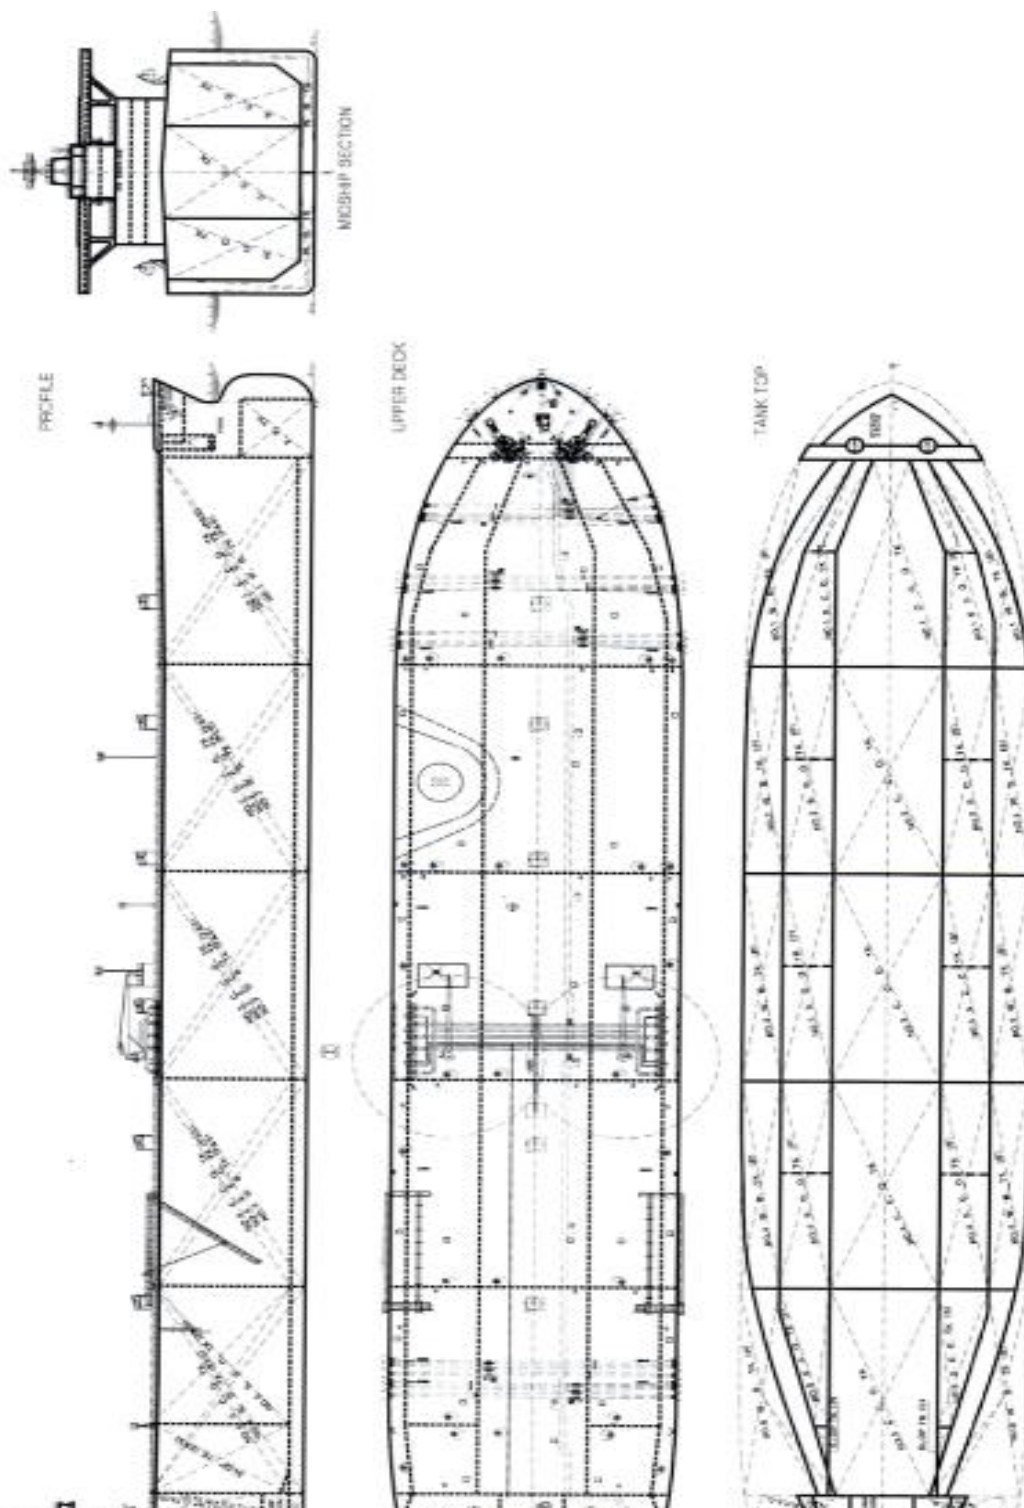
Креслення перерізів корпусу танкера Eagle Vancouver
